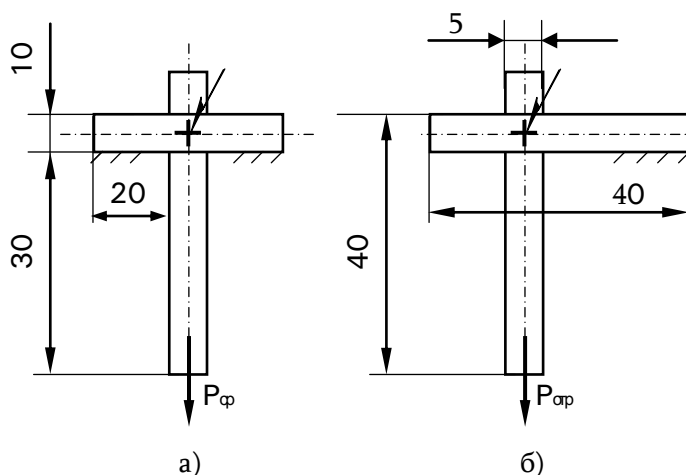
Схемы испытания сварных соединений на срез (а) и на отрыв (б)
